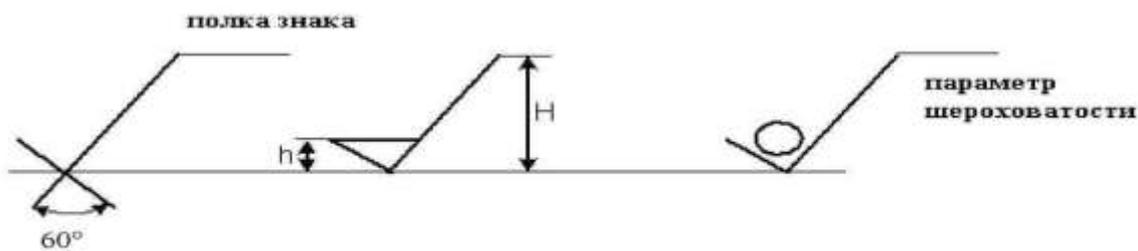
Изображение знаков, обозначающих шероховатость поверхностей
